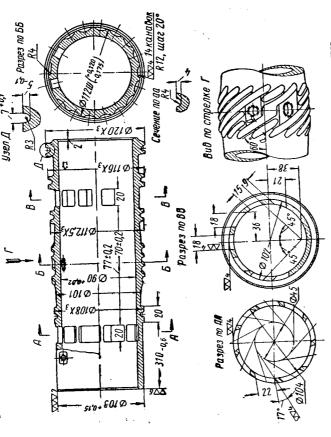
Корпус компрессорного цилиндра и продувочного насоса с воздушным охлаждением дизель-компрессора 1ДК.
